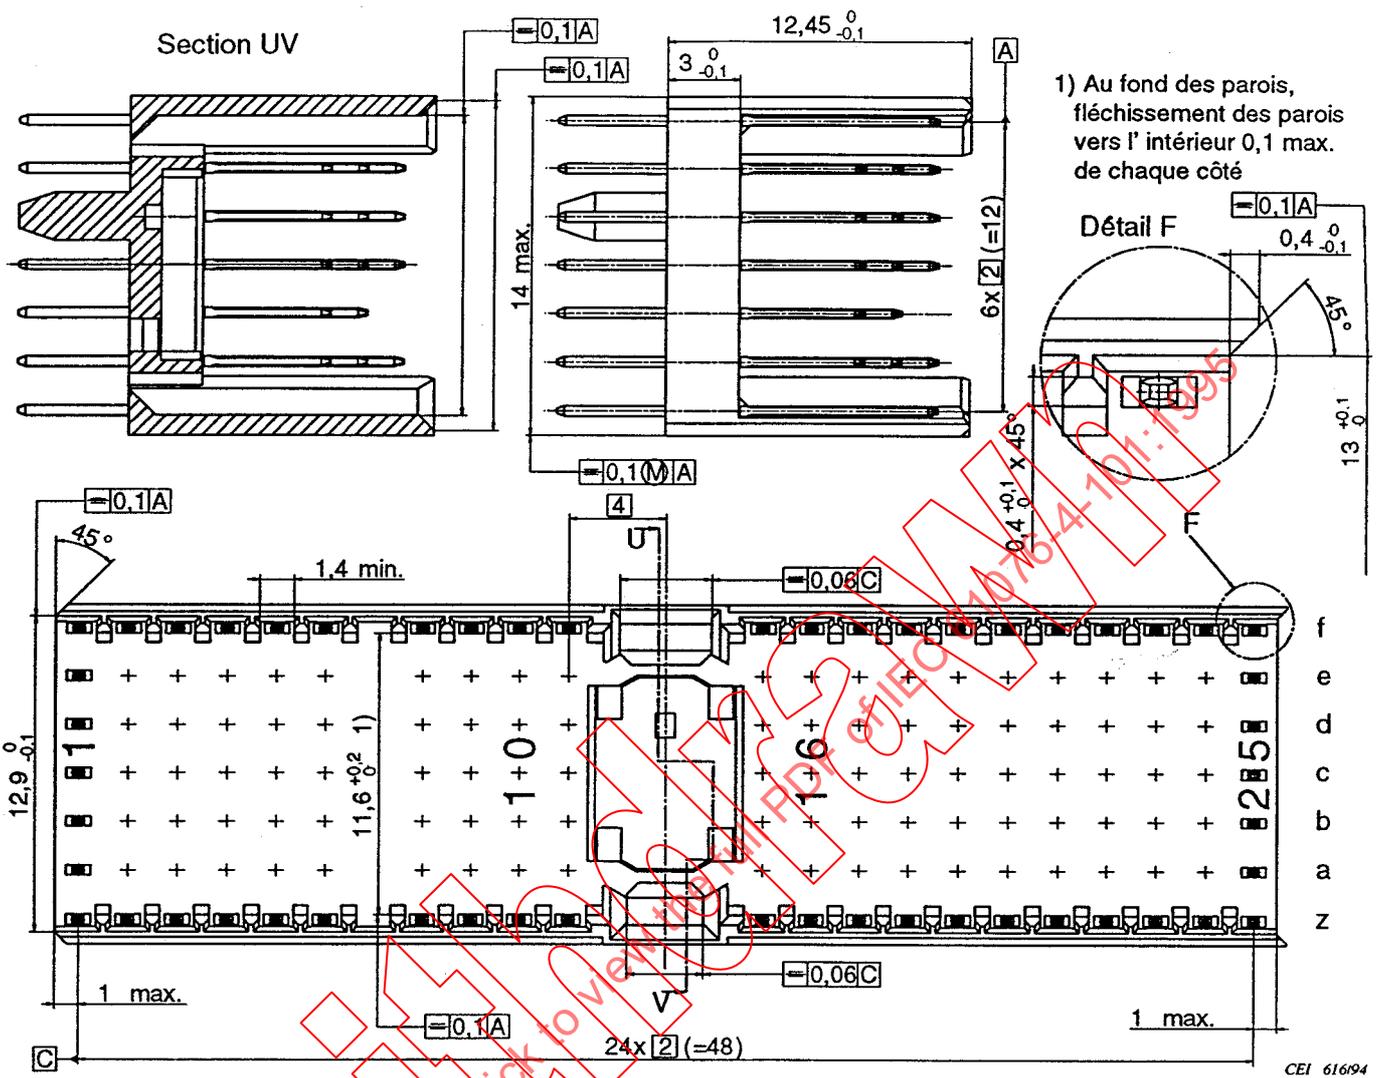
Dimensions du modèle A, module d'embase 50 mm avec BMF
